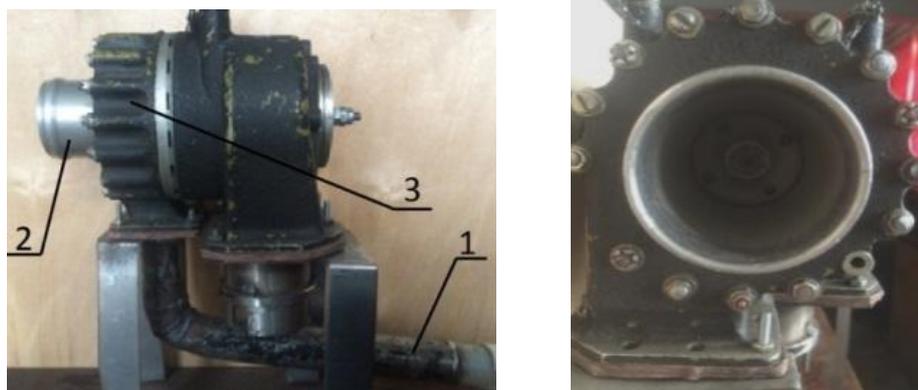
Общий вид турбины: 1 – входной патрубок; 2 – выходной патрубок; 3 – корпус
